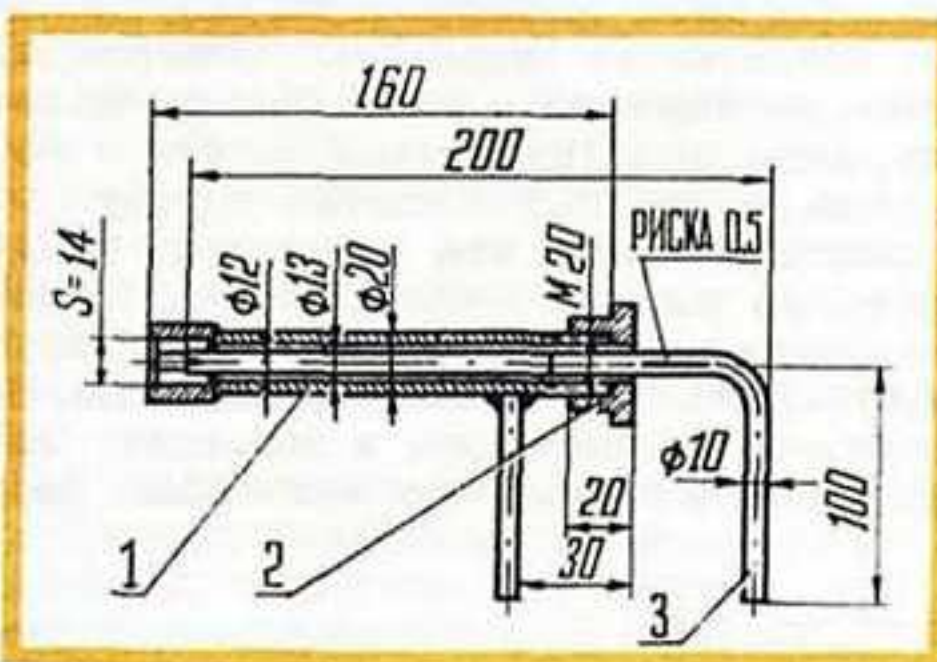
Ключ для регулировки клапанов в сборе: 1 — трубка с торцовым ключом; 2 — втулка; 3 — стержень.
